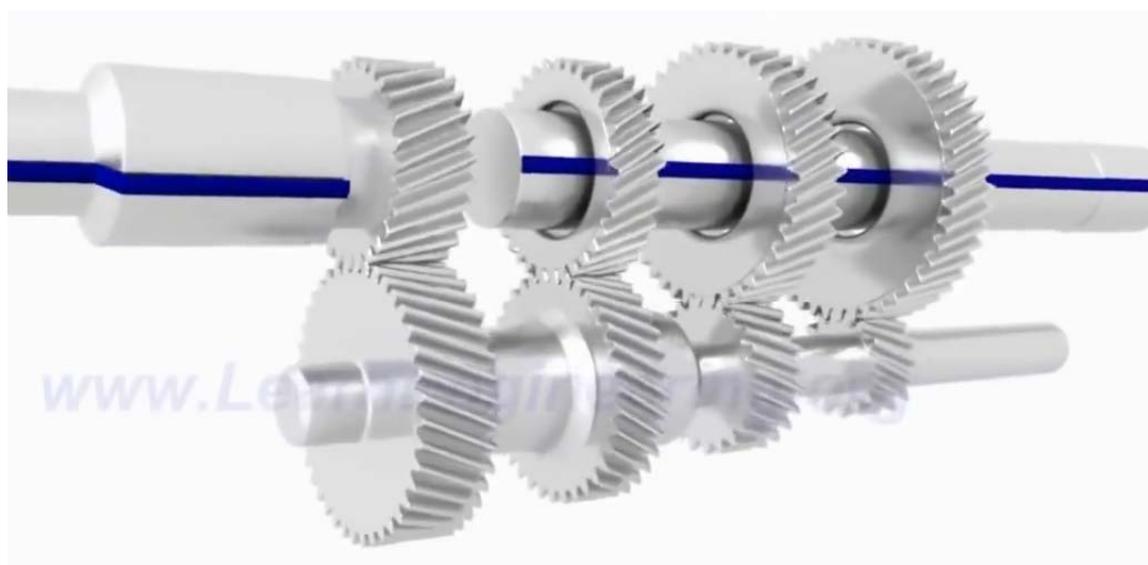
схема коробки передач с постоянным зацеплением шестерней.
